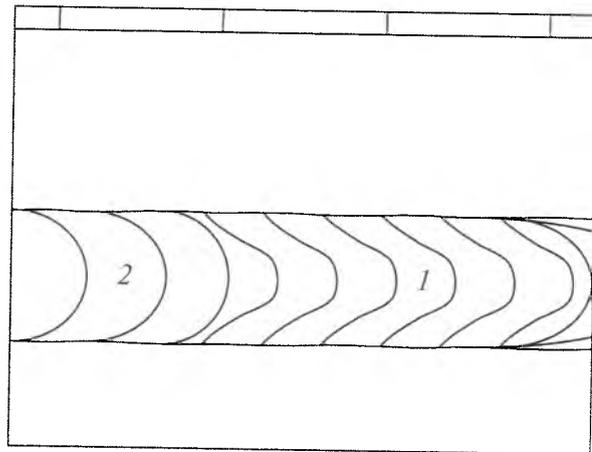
Стыковое сварное соединение трубопровода. Ручная дуговая сварка. Поверхность шва равномерная. Ширина шва порядка 8–10 мм. В кратере на участке гашения дуги наблюдается шлаковое включение 1
